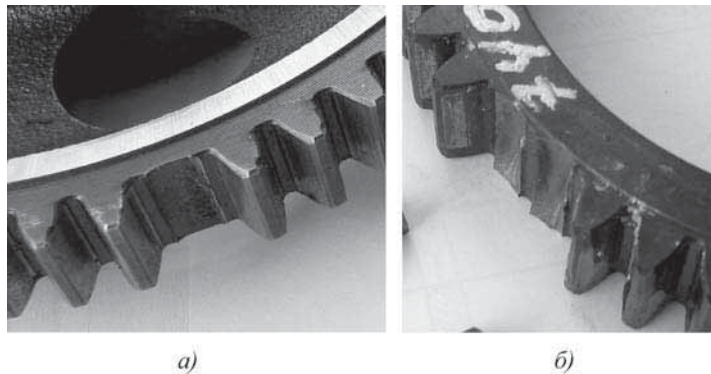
Усталостное разрушение зубьев промежуточной шестерни (а) и шестерни коленчатого вала (б)
